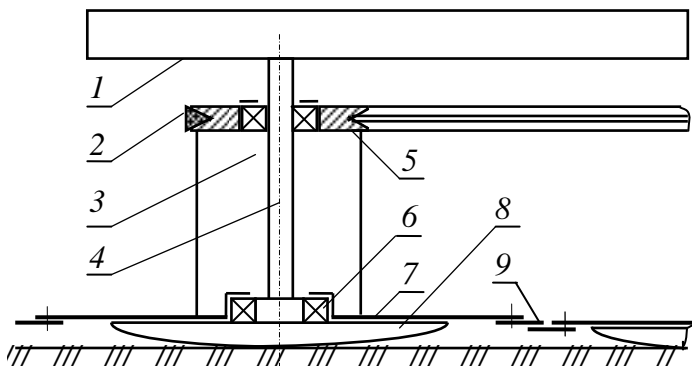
Схема ротора двухроторной косилки с механическим приводом.
